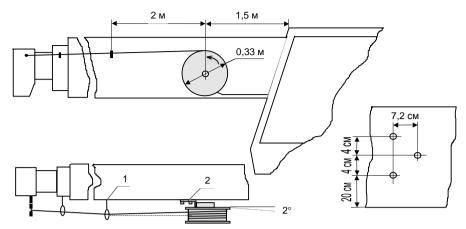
Установка датчика длины и разметка мест его крепления
